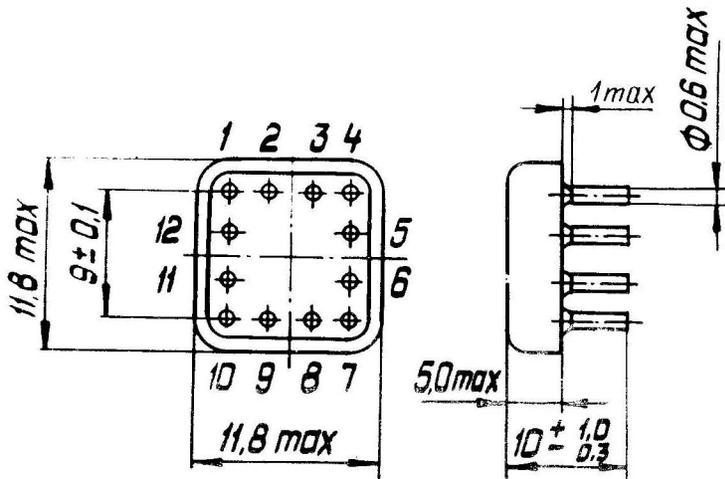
Прямоугольный металлополимерный корпус "Тропа", 12 выводов.
